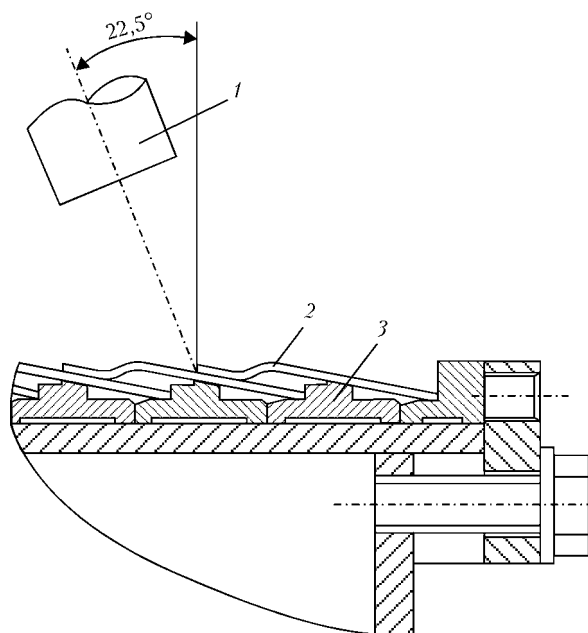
Схема выполнения сварки блока обечаяк: 1 — электронно-лучевая пушка; 2 — блок обечаяк; 3 — сборочно-сварочное приспособление
